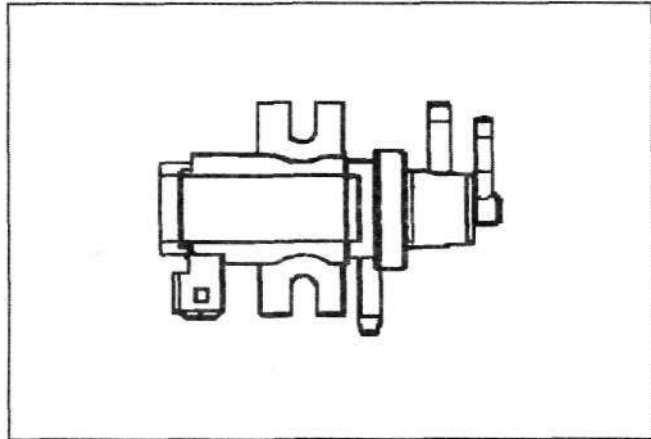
Электромагнитный клапан привода турбокомпрессора.
